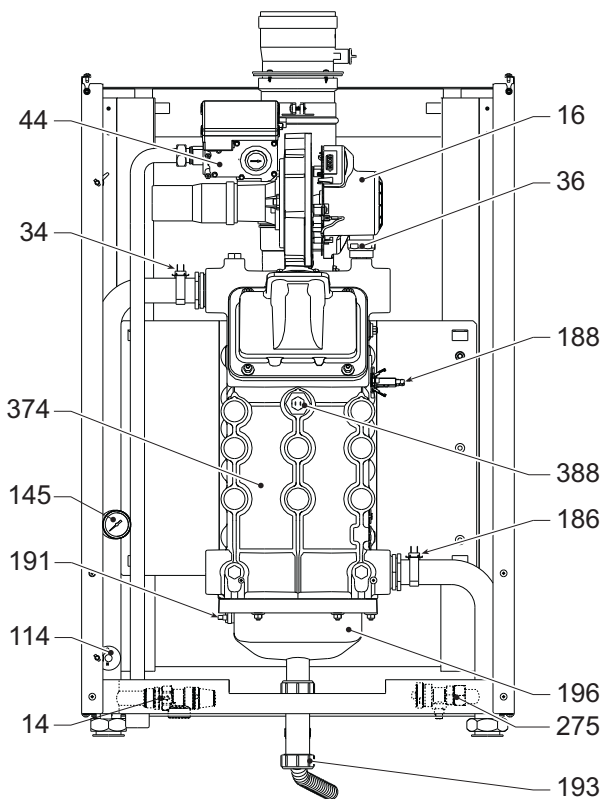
Vue générale mod. TORO W 60 et TORO W 80
